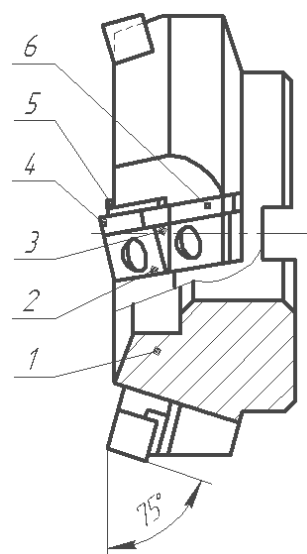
Торцева фреза з механічним кріпленням різальних пластин з твердого сплаву
